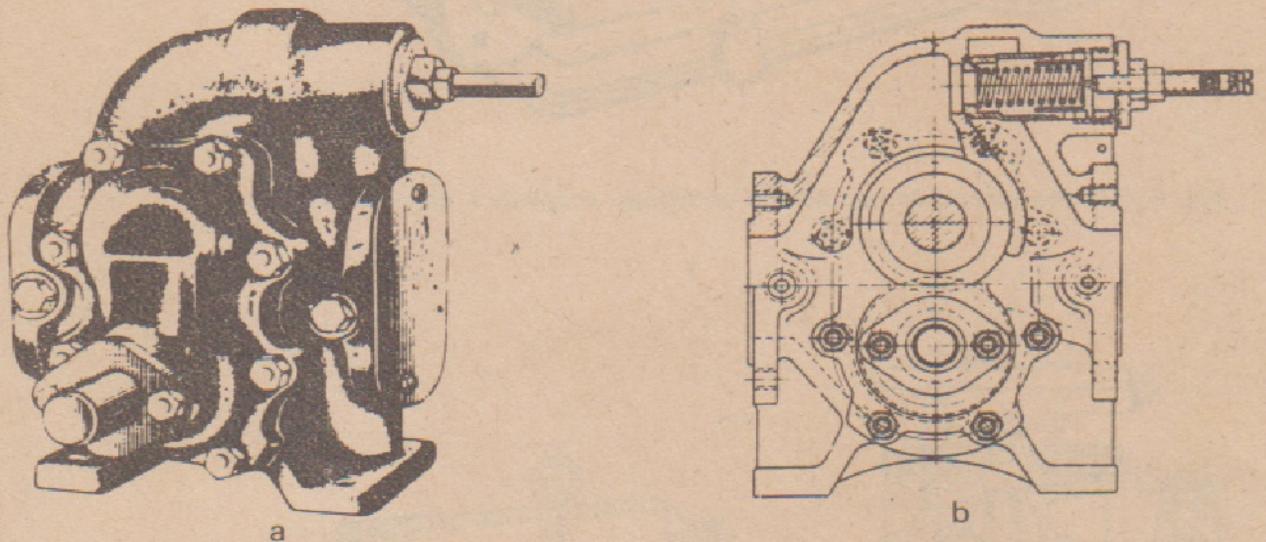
Bomba de engranaje: a) aspecto exterior; b) corte transversal
